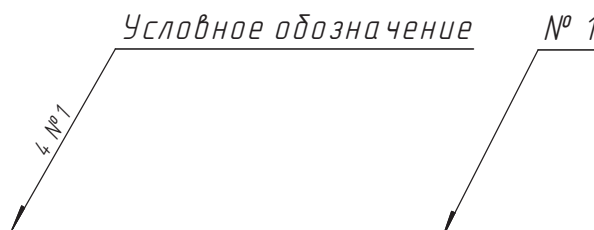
Обозначения однотипных сварных швов
